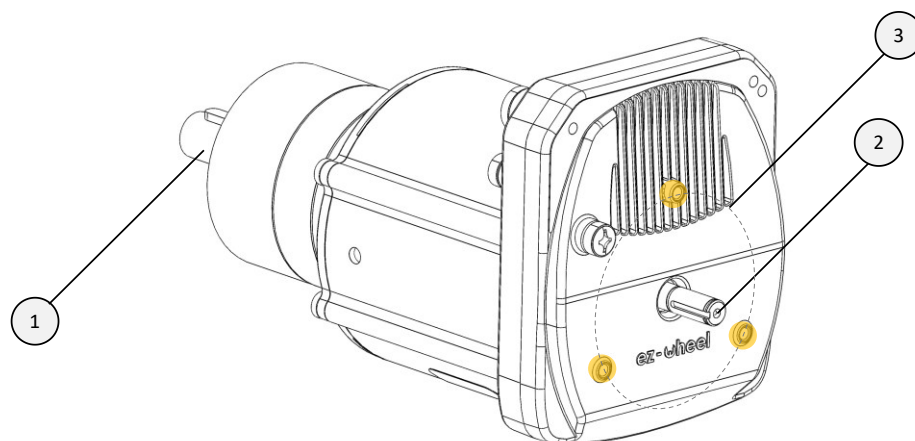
Vue d'ensemble des interfaces mécaniques – SWD® Core
